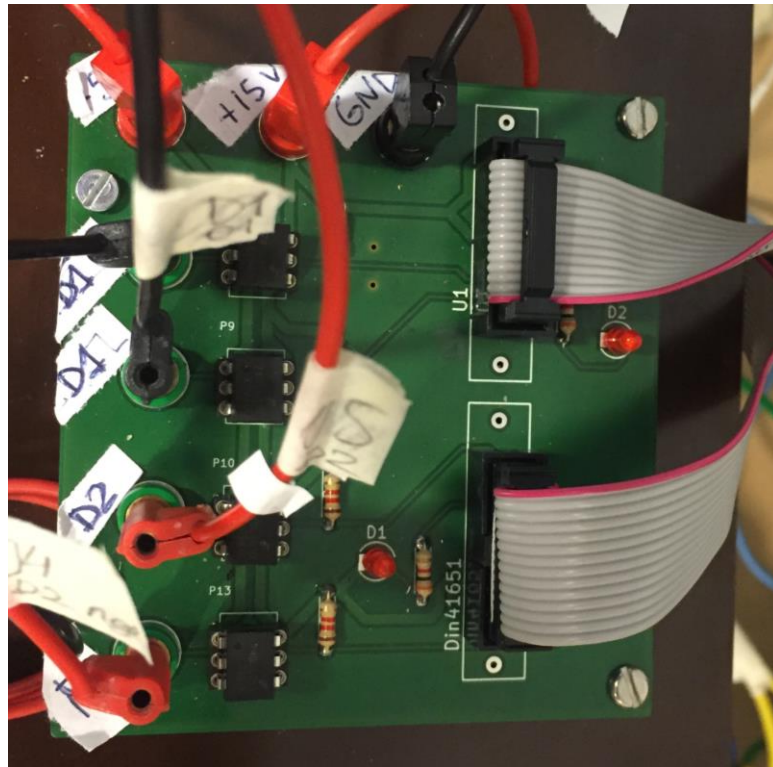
PCB Acoplamiento a Driver – Salidas montado
